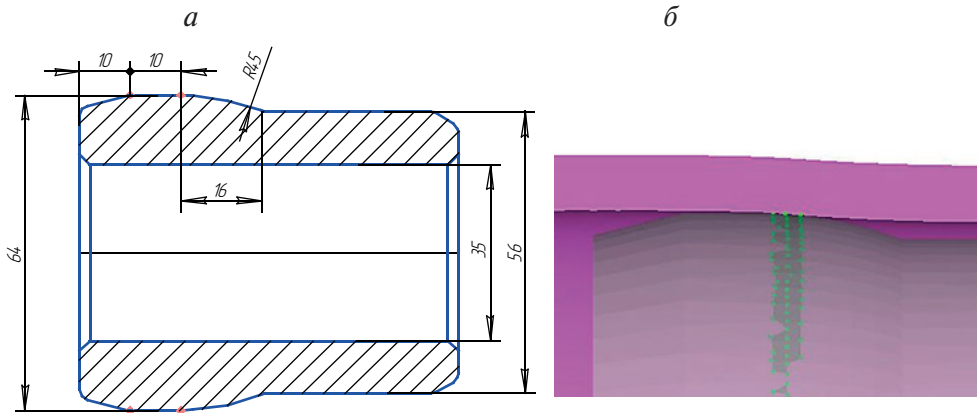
Оправка со сферическим участком рабочей поверхности — *а* и длина контакта внутренней поверхности трубы с рабочей частью оправки — *б
